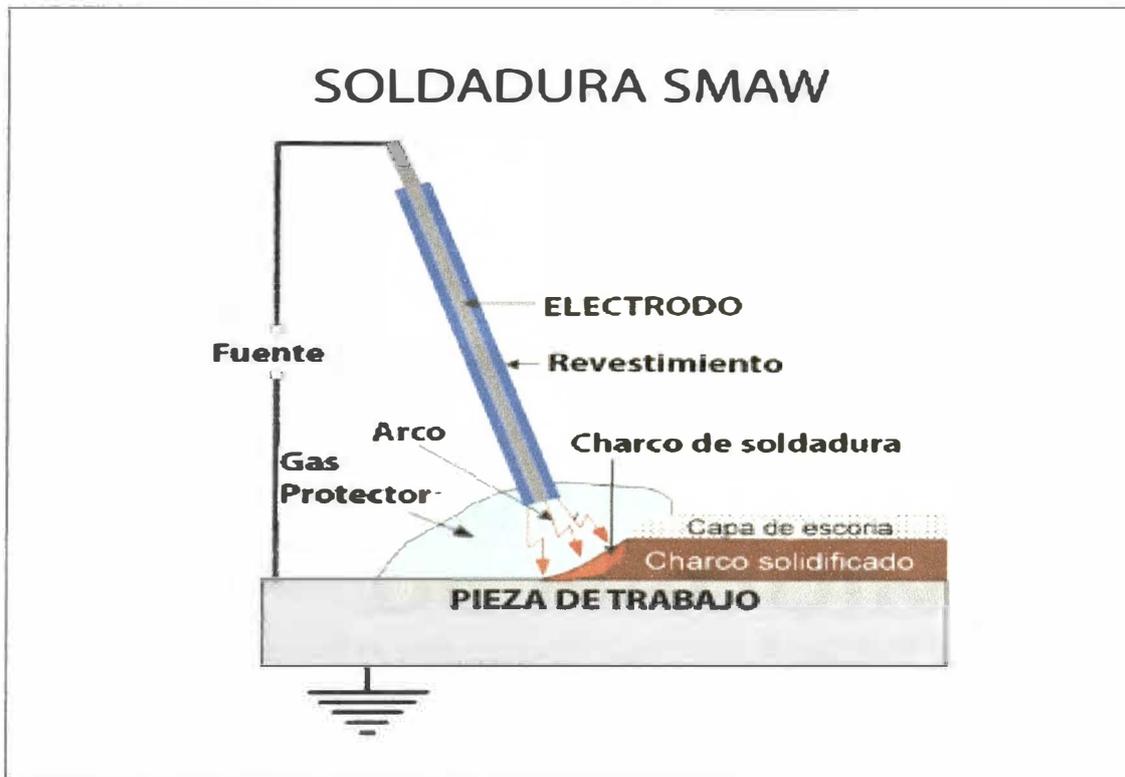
Soldadura SMAW. (Fuente: <http://www.demaquinasyherramientas.com/>)
